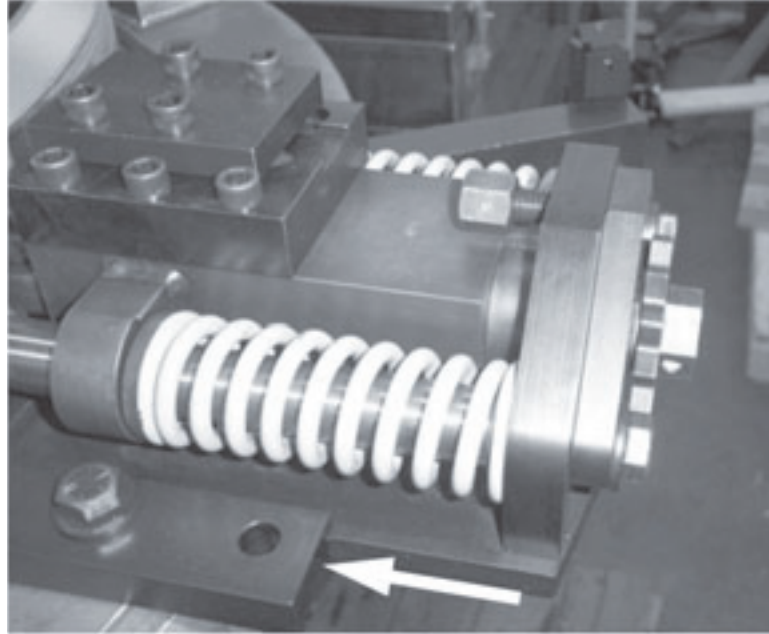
Faites glisser l'embase du plateau porte-outil dans les rainures des blocs de montage des plateaux jusqu'à ce que la roue suiveuse vienne en contact avec la surface du tuyau.
